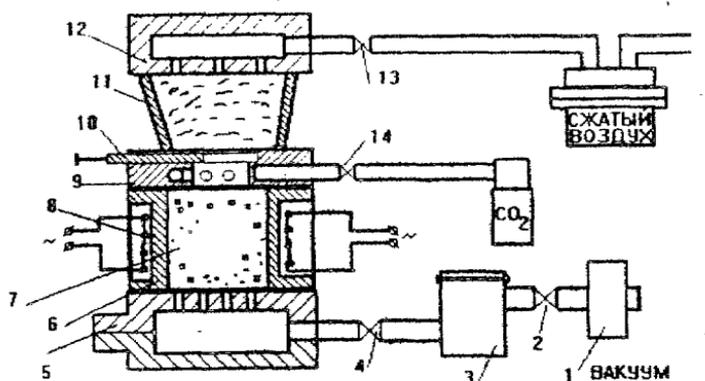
Схема промышленной установки для комбинированного изготовления стержней: 1 - вакуумнасос; 2, 4, 13, 14 - кран; 3 - вакуумный ресивер; 5 - вакуумная камера; 6 - стержневой ящик; 7 - стержень; 8 - электронагреватель; 9 - вдувная головка; 10 - шибер; 11 - передвижной резервуар; 12 - воздуходувная головка
